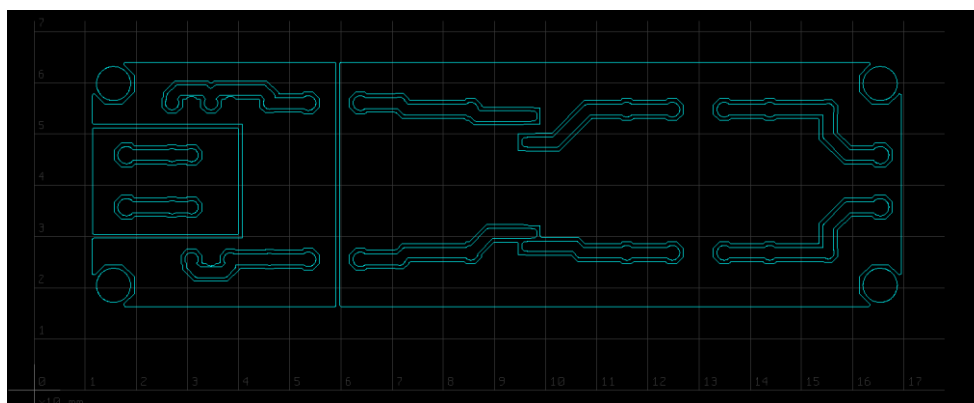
Simulation de la couche PCB dans RoutePro3000.
